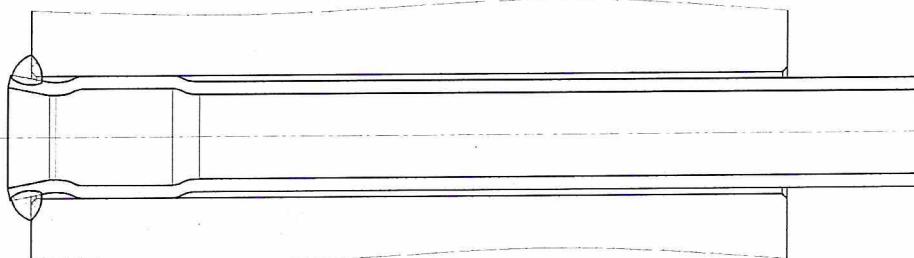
Развальцовка конца трубы за сварным швом
